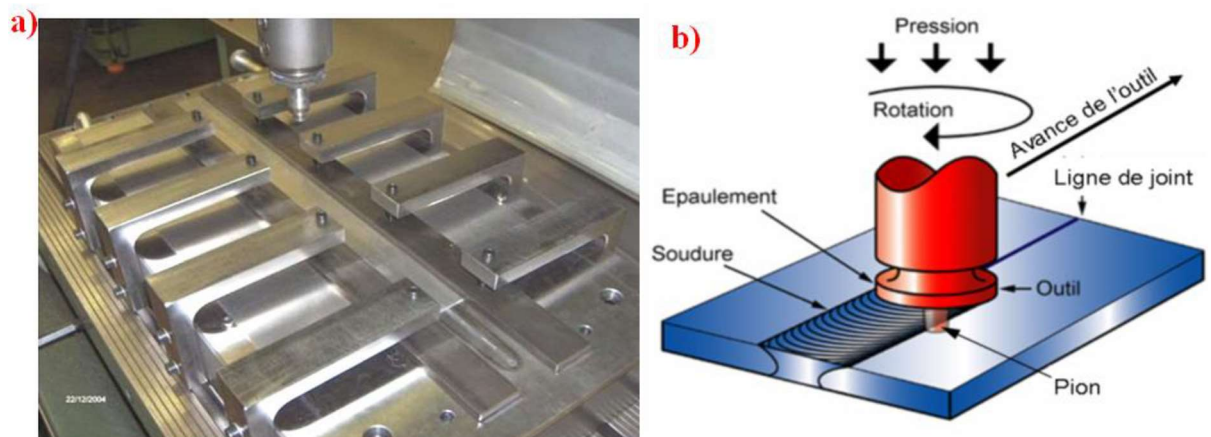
a) Exemple de système de bridage [7]. b) Illustration du procédé de soudage par friction et malaxage [8].
